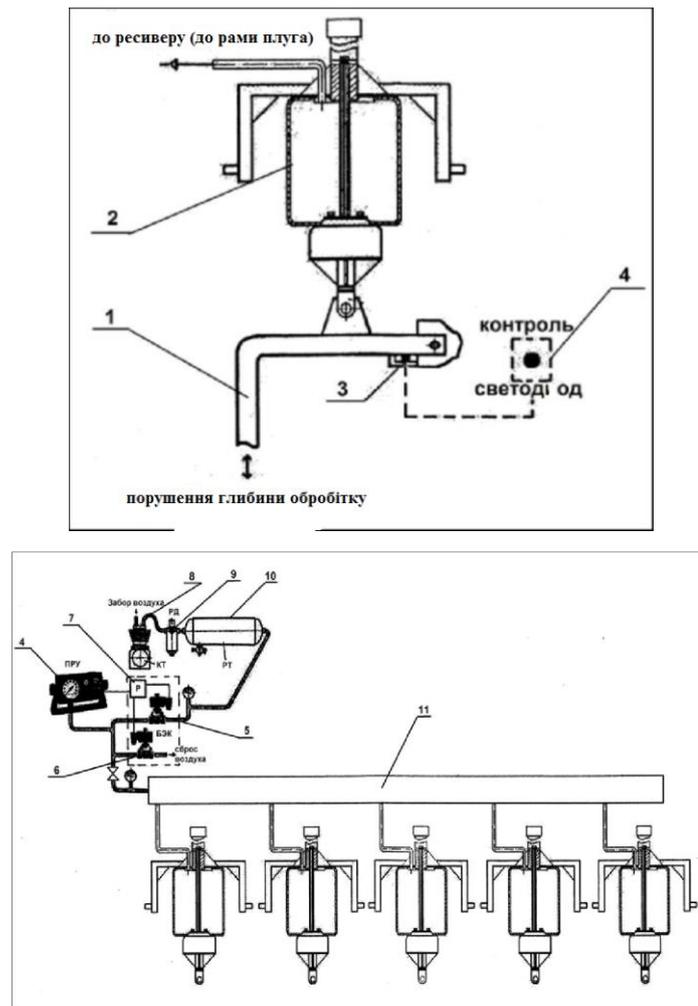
Схема керування пневматичною запобіжною системою плуга: 1 - стійка корпусу плуга; 2 – пневматичний запобіжник; 3 – контактна пластина; 4 – світлодіод на пульті керування; 5 – впускний електромагнітний клапан; 6 – випускний електромагнітний клапан; 7 – блок із реле управління; 8 – компресор трактора; 9 – регулятор управління; 10 – ресивер; 11 - резервна ємність запобіжної системи плуга.
